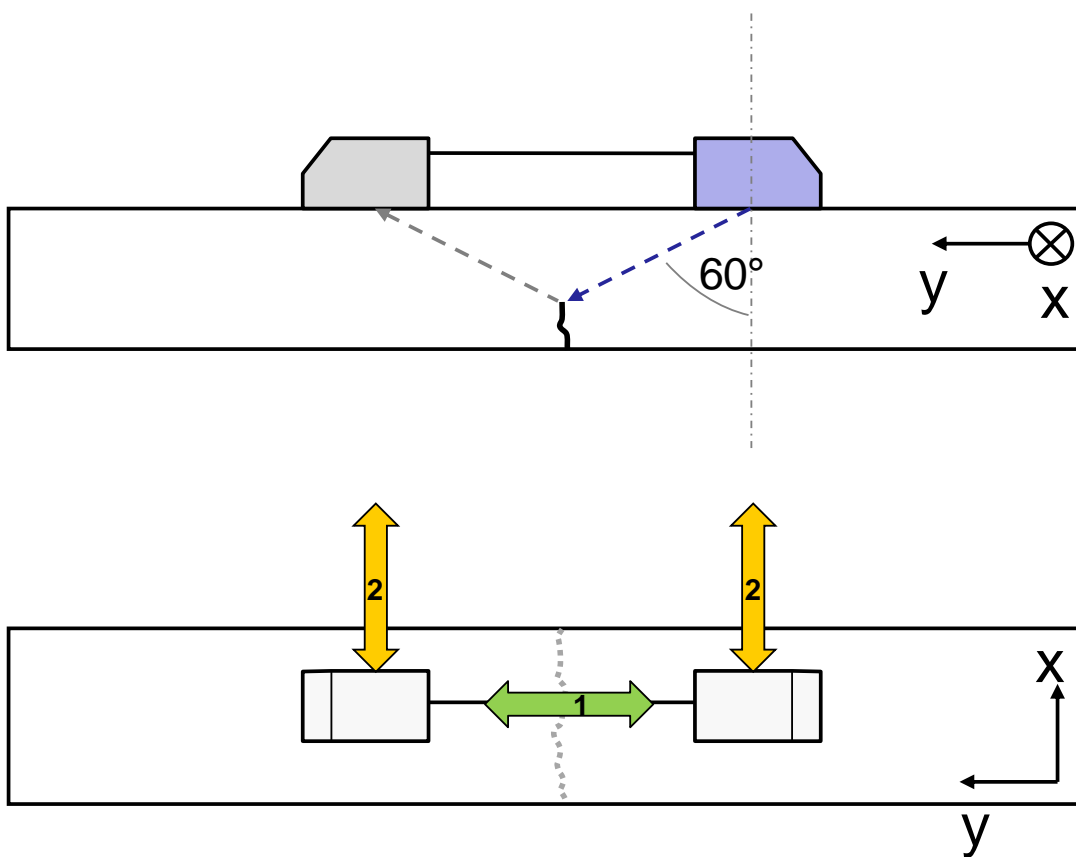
Prüfanordnung Ultraschall-TOFD Prüfungen; Seitenansicht (oben) und Ansicht von oben (unten) mit Angabe der Scanrichtungen 1(senkrecht zur Schweißnaht) und 2 (parallel zur Schweißnaht)
